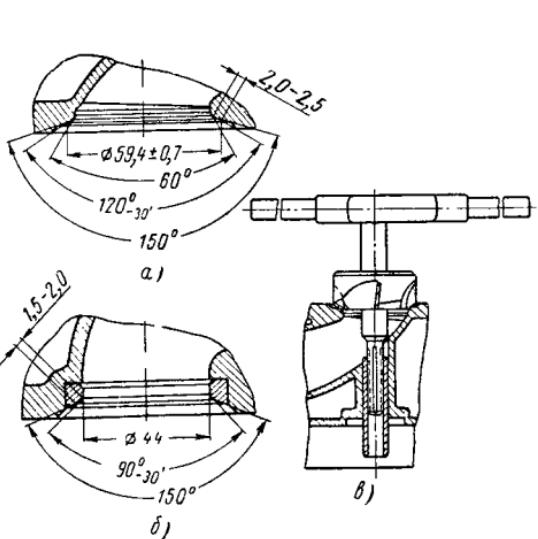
Седла клапанов и установка инструмента при их обработке:
